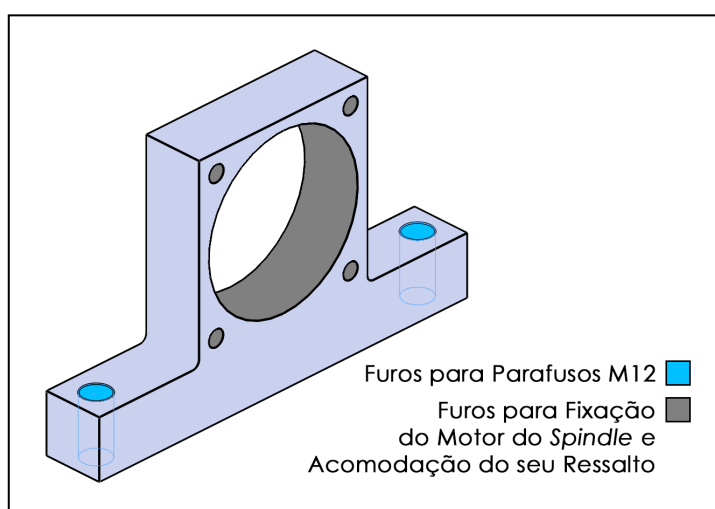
Ilustração do suporte do motor do *spindle* do mini-torno CNC, que permite a fixação do motor no carro móvel do eixo Z.
